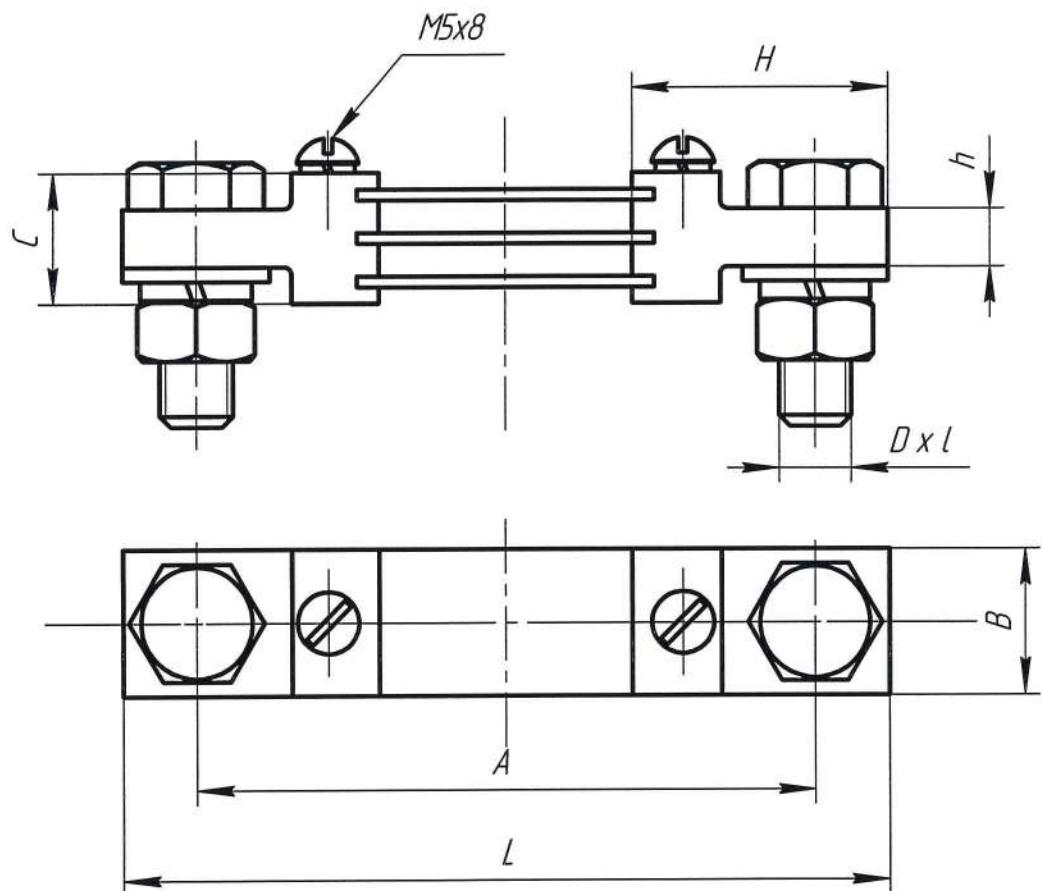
Габаритные размеры шунта 75 ШИСВ на токи 60, 75, 100 А
